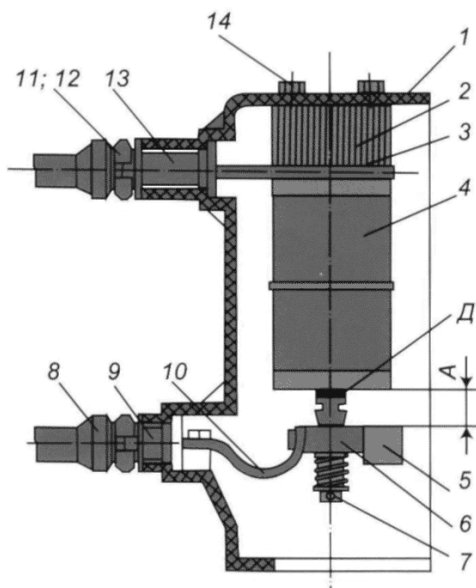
Полус выключателя ВВЭ-10: 1 - корпус изоляционный; 2 - крышка ребристая (только для 1600 А); 3 - токоотвод верхний; 4 - ВДК; 5 - радиатор (только на ток 1600 А); 6 - контакт подвижный; 7 - узел поджатия; 8 - контакт розеточного типа выдвижного элемента; 9, 13 - стержень контакта; 10 - связь гибкая; 11, 12 - шайба и гайка; 14 - болт; А - разность хода подвижных контактов выключателя; Д - зона поджатия контакта
